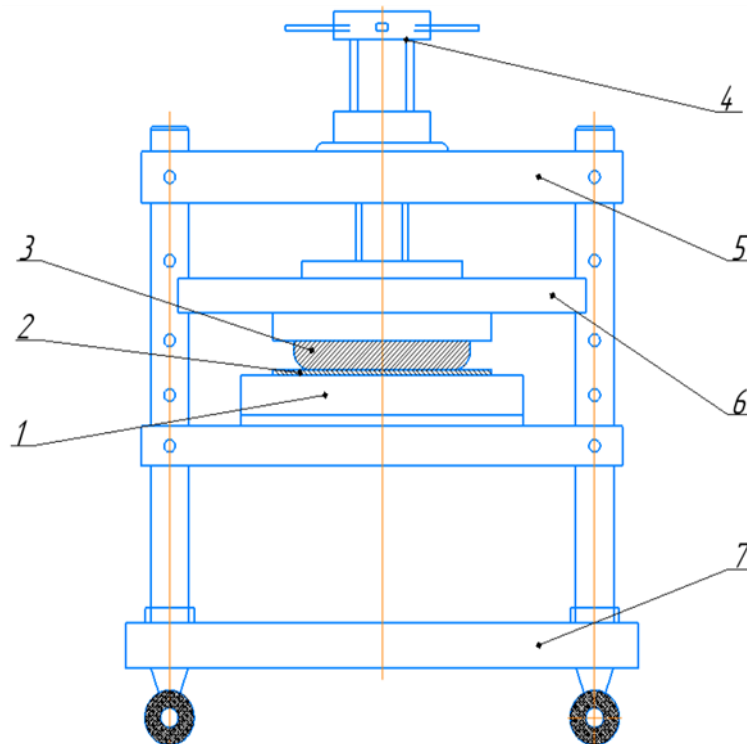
Схема прессы портального типа с механическим приводом:
